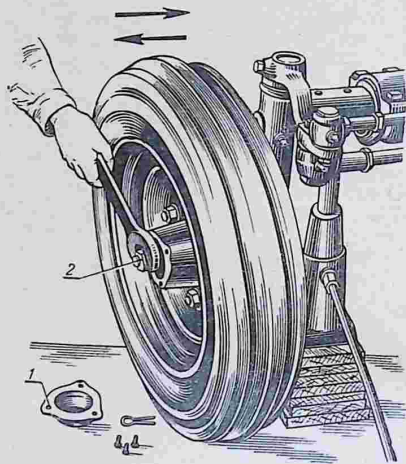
Проверка и регулировка зазора в подшипниках направляющих колес:
